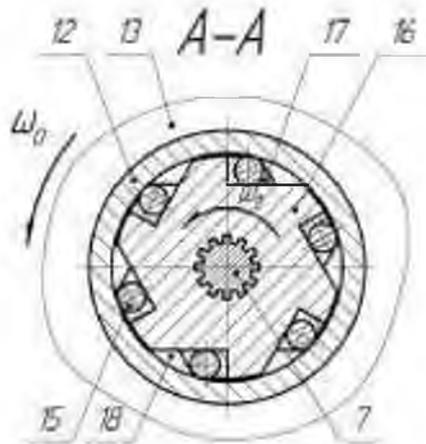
Схема предлагаемой конструкции дифференциала (вид А-А)
